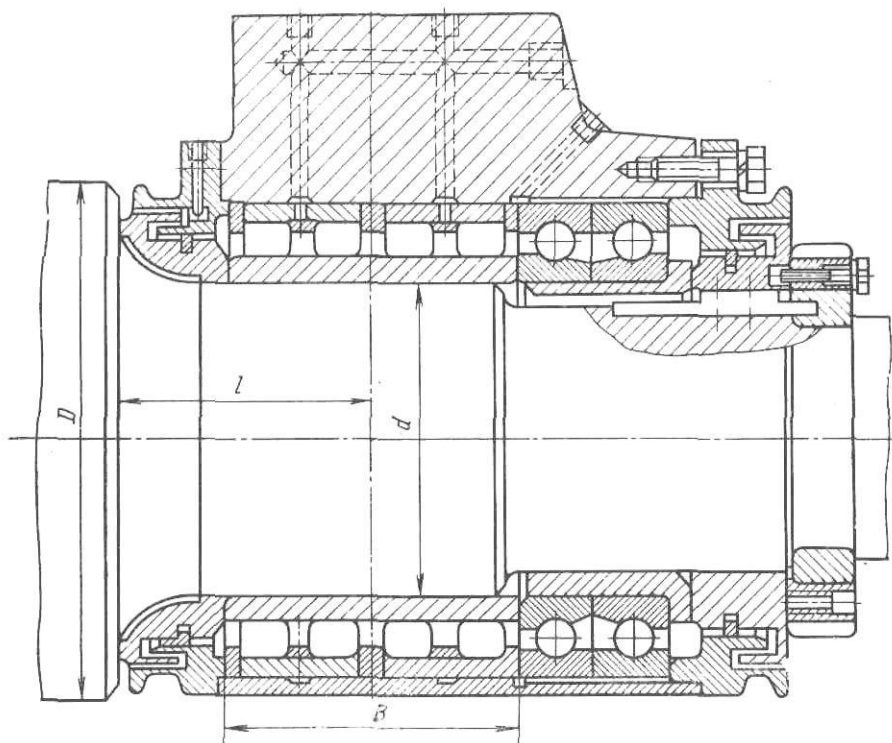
Фиксирующая опора валка на четырехрядном подшипнике с цилиндрическими роликами (шейка валка коническая или цилиндрическая с диаметром под подшипник 500—950 мм)
